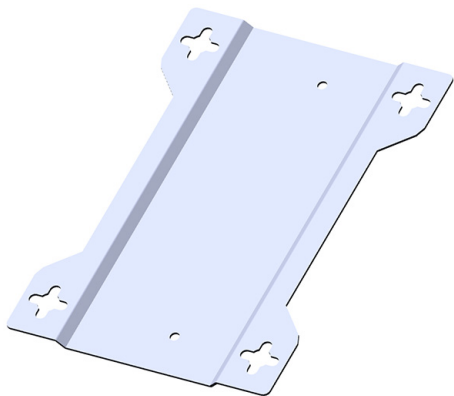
Adapterplatte für die Wandmontage eines 3D Profile Unit - 2
